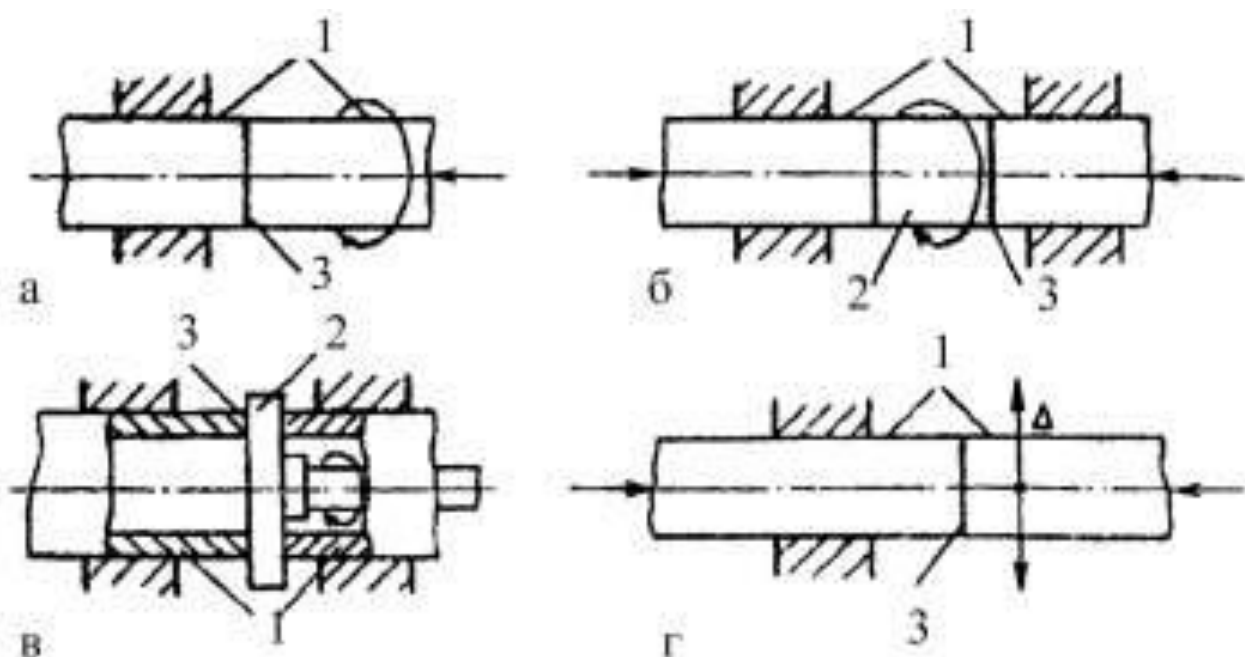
Схемы процесса сварки трением: 1 - свариваемые детали; 2 - вставка; 3 - зона сварки
